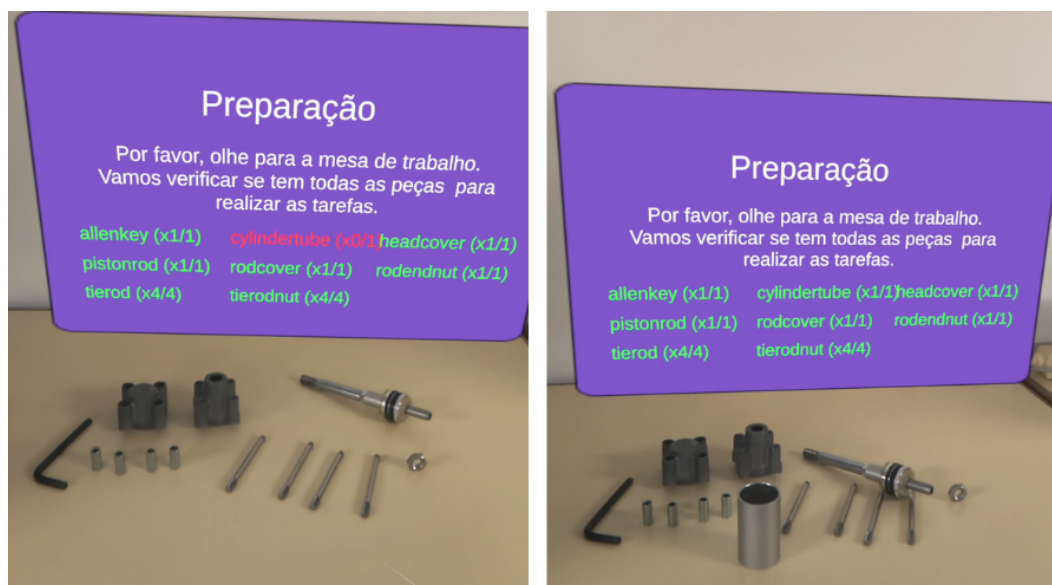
Fase de preparação na aplicação de instrução virtual
